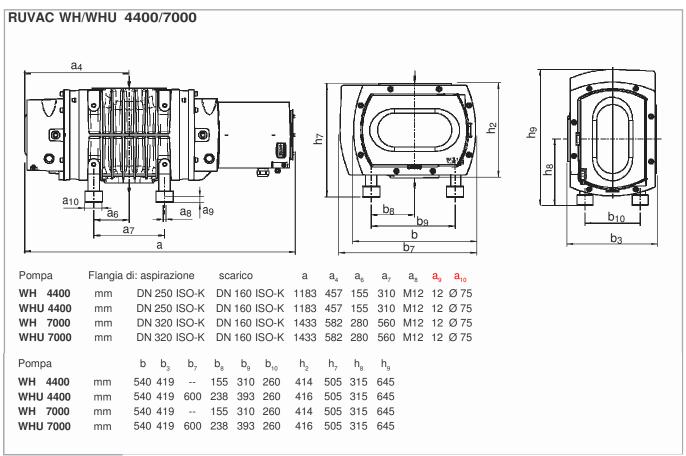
Disegno dimensionale per RUVAC WH/WHU 4400 e 7000
